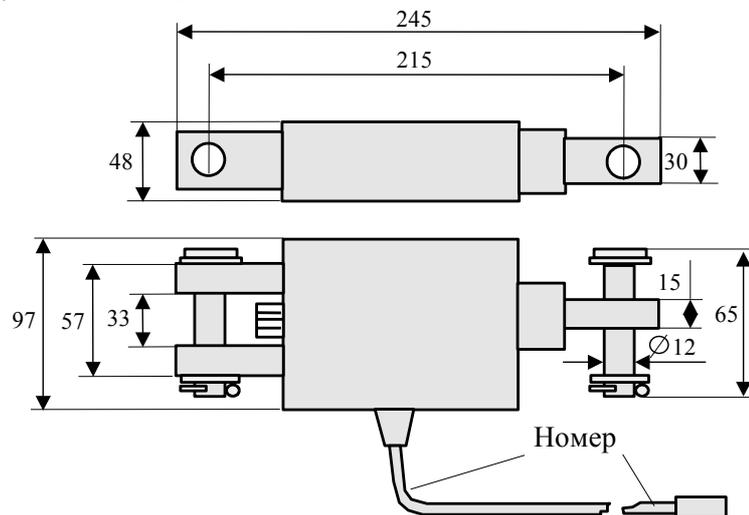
Габаритные и присоединительные размеры ПрУ
